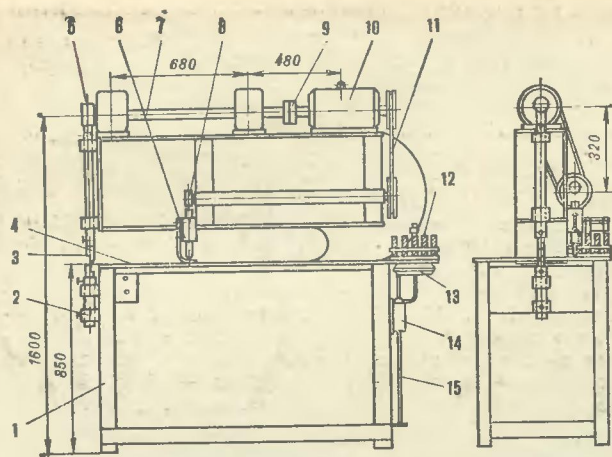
Механические ножницы: 1 — рама, 2 — нижний, неподвижный нож, 3 — верхний, подвижной нож, 4 — стол, 5 — кривошип, 6 — резак для картона, 7 — вал, 8 — эксцентрик, 9 — соединительная муфта, 10 — электродвигатель, 11 — клиноременная передача, 12 — пневматический пресс, 13 — пневмокамера, 14 — пневмокран, 15 — тяга с педалью.
